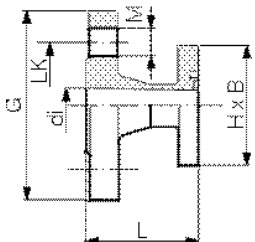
Dimensiones de la parte frontal del sensor DN 2...25
